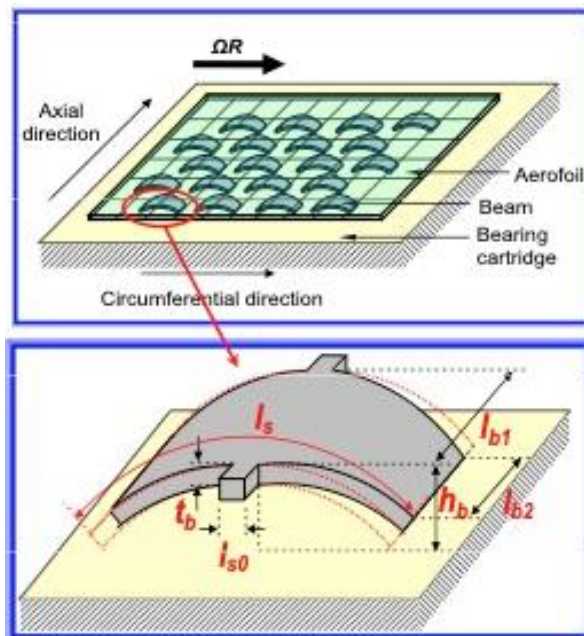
Dimensionado de los cojinetes de aire patentados [31].
